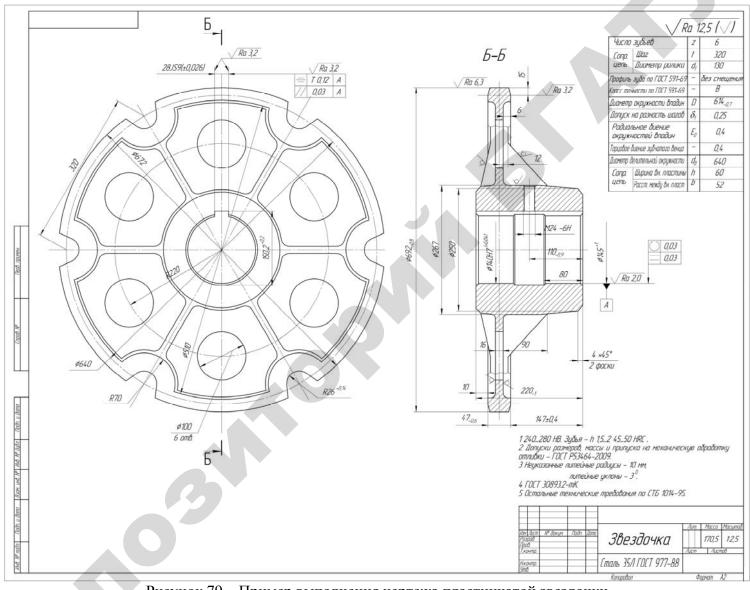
Пример выполнения чертежа пластинчатой звездочки
